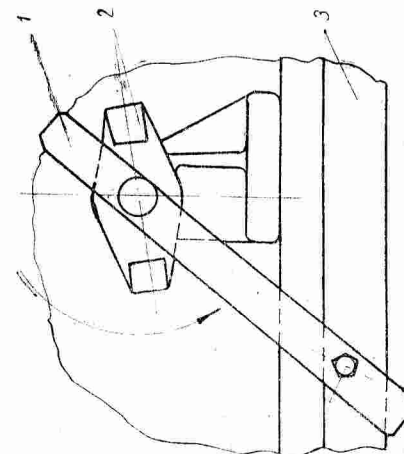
Установка упоров для транспортировки выключателей ВМ-35-600 и ВМД-35-600:
